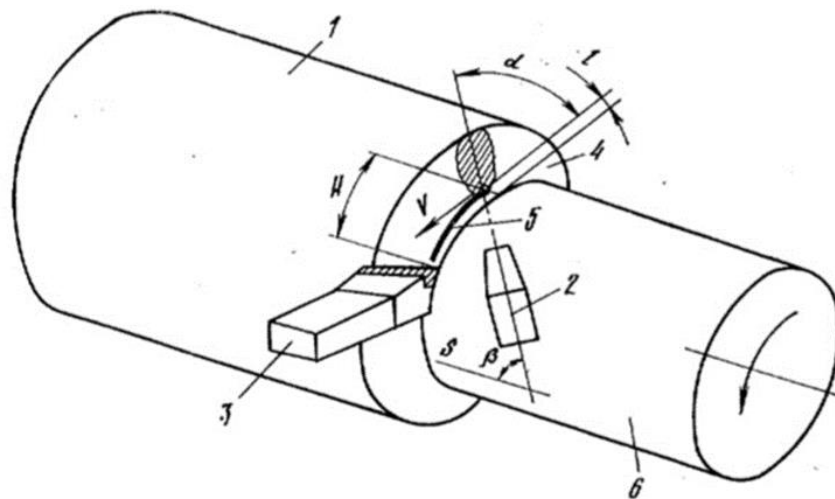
Способ механической обработки с подогревом, где 1 – обрабатываемая заготовка, 2 – плазматрон, 3 – резец, 4 – плоскость резания, 5 – образующаяся канавка, 6 – обработанная поверхность [57-59]
